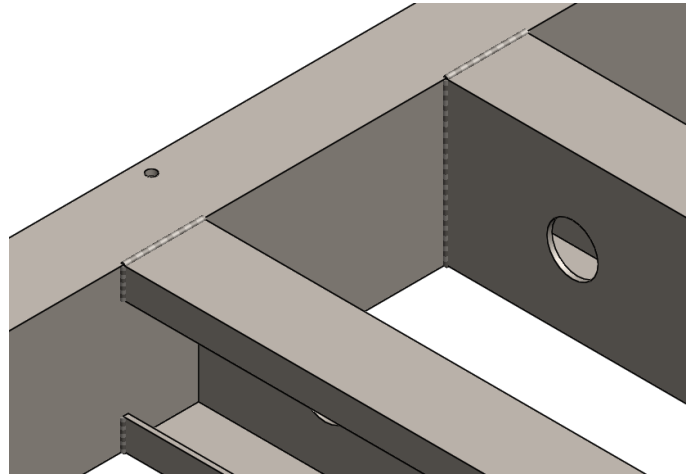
Perfil c soldado con perfil tubular rectangular
